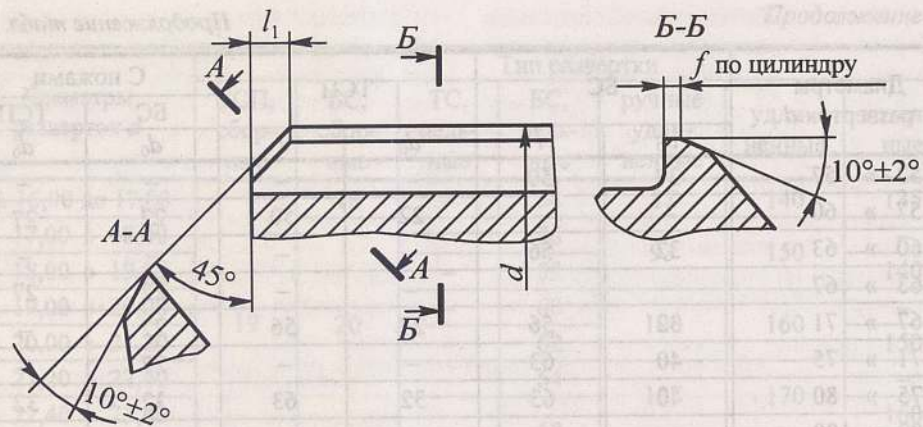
Развертка с совмещенными заходным и режущим участками
